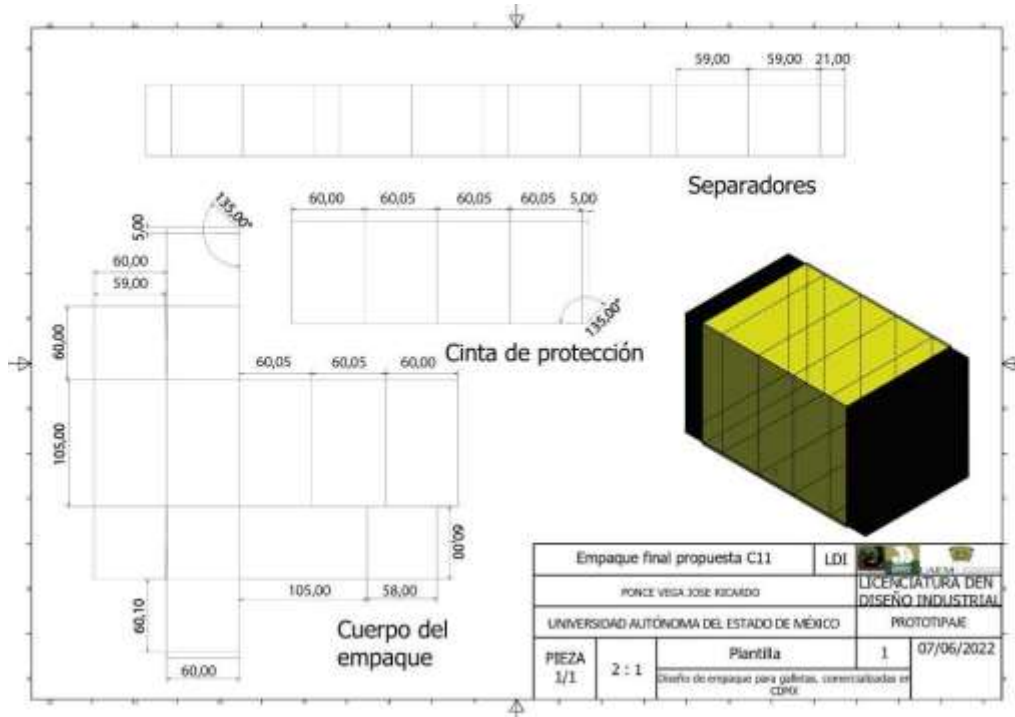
Plantilla del empaque, (fuente propia 2022).
